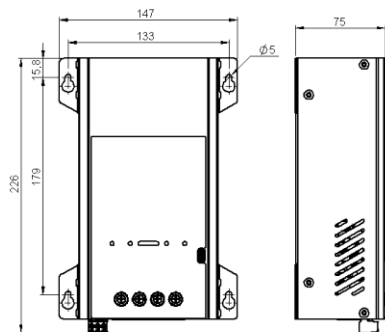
Dimensões do Equipamento SCORPION MAX.
